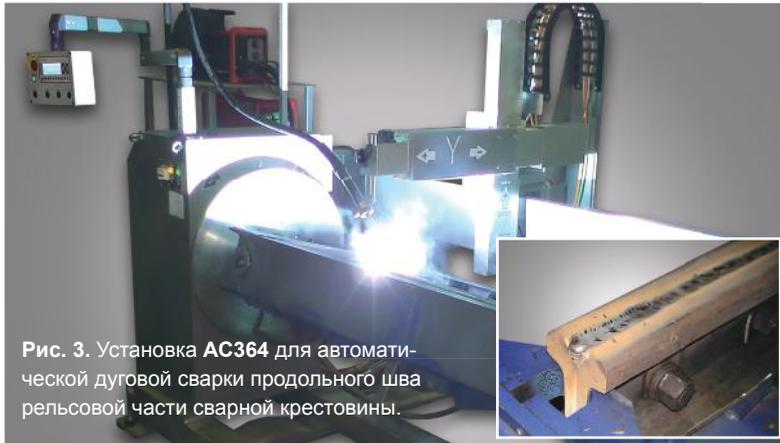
Установка АС364 для автоматической дуговой сварки продольного шва рельсовой части сварной крестовины.
